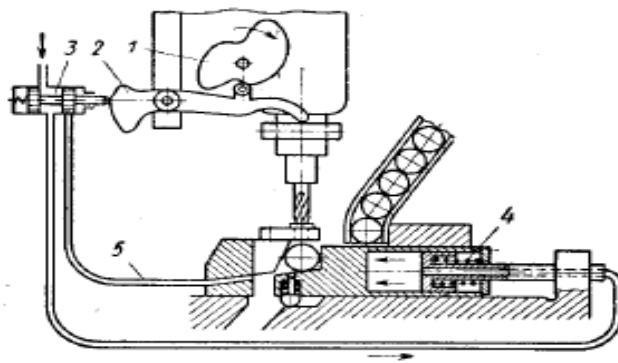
Схема автоматизованого пневматичного кондуктора для свердління отворів у втулках
